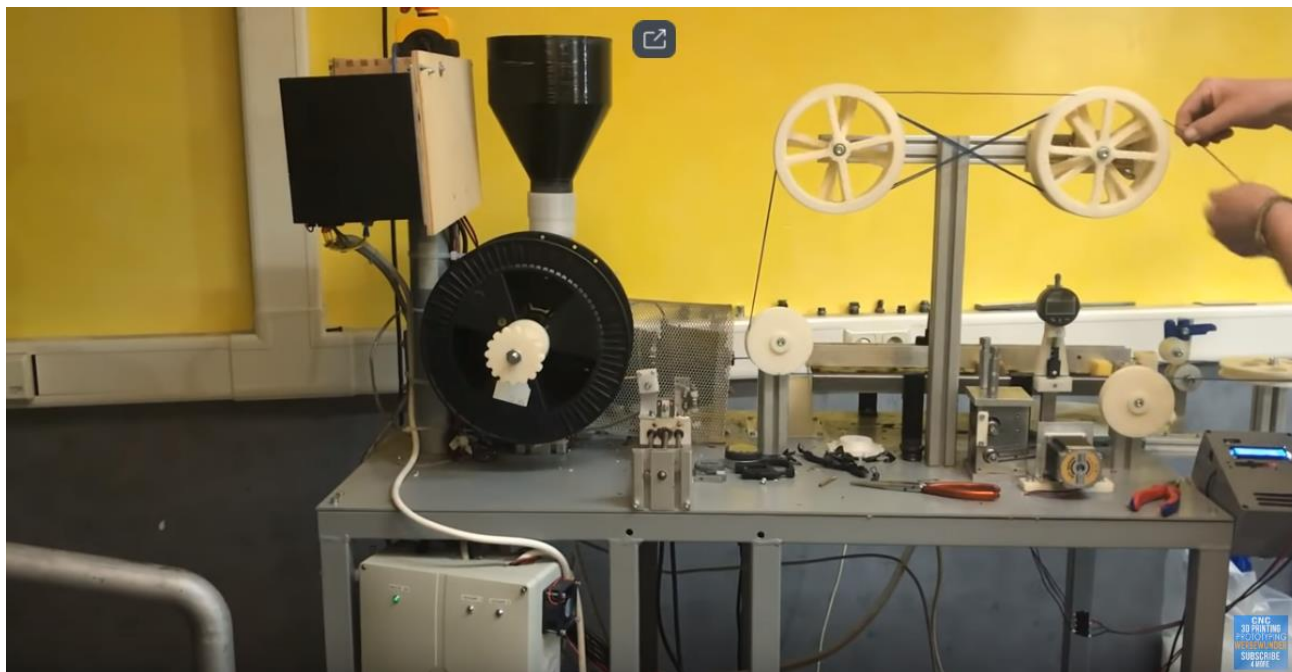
Екструдер з елементами контролю для виготовлення ниті
